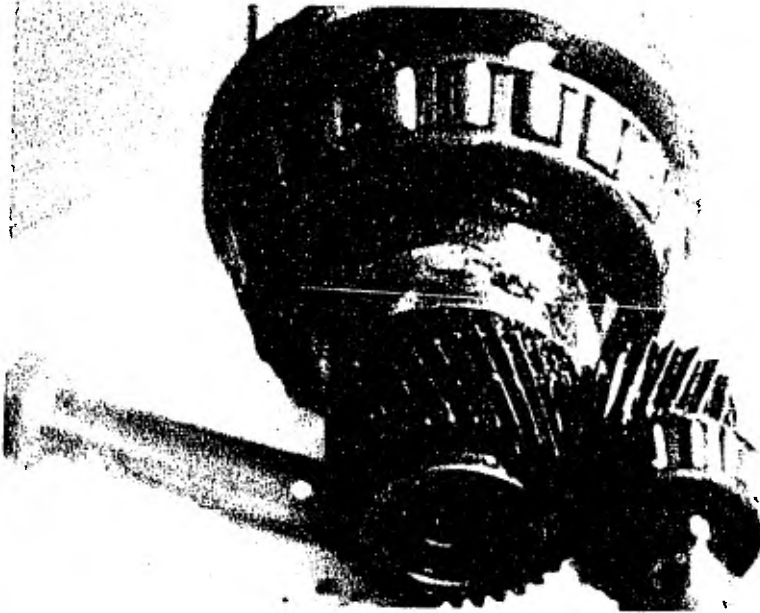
Detalle del engranaje de la Flecha Acopladora con la Flecha - de Salida.
